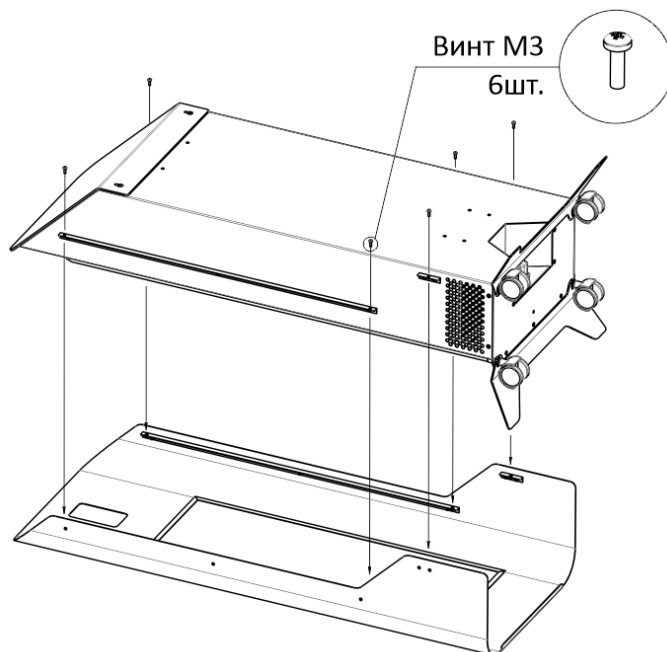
Схема разборки корпуса и передней панели рециркулятора.
